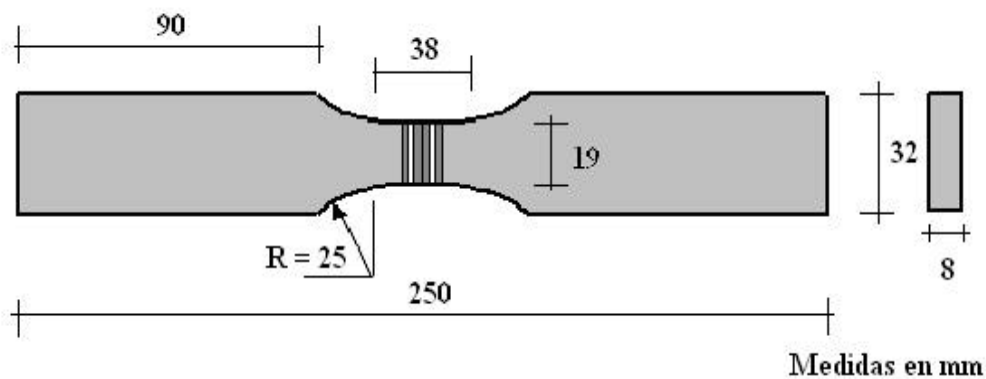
Diseño de probeta para ensayo de tracción de la junta soldada según la regla QW 462.1(a) del Código ASME sección IX.
